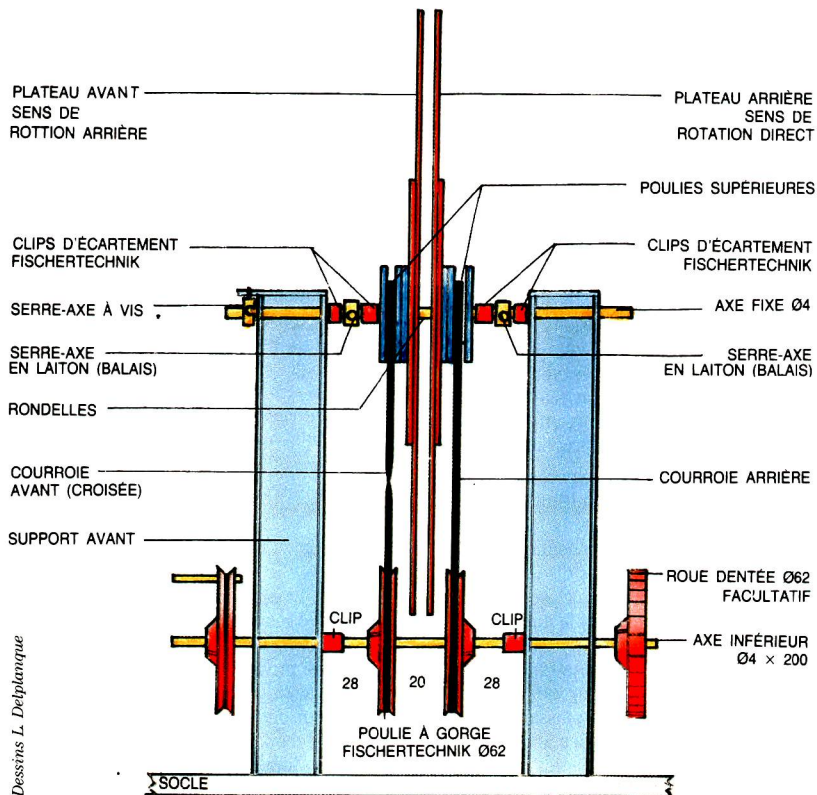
MONTAGE MÉCANIQUE AVANT-ARRIÈRE
